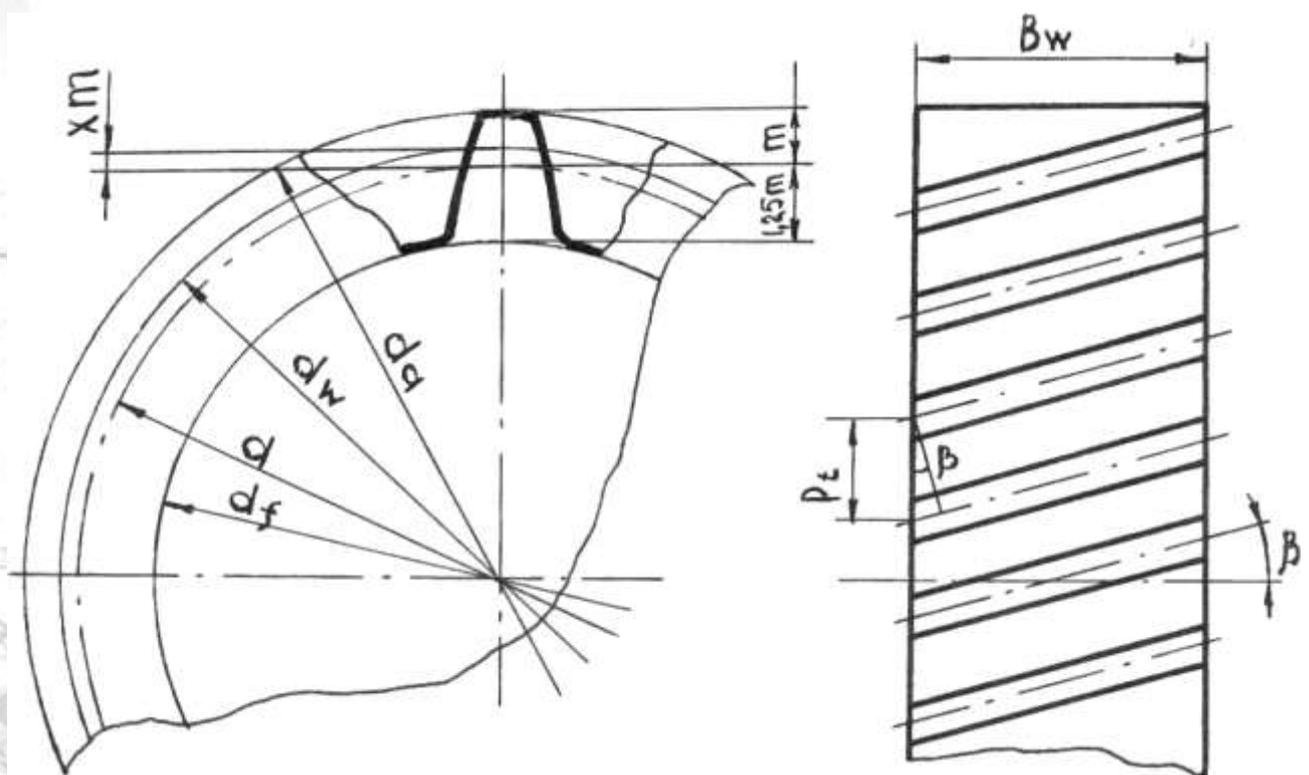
Основные размеры косозубого цилиндрического колеса
